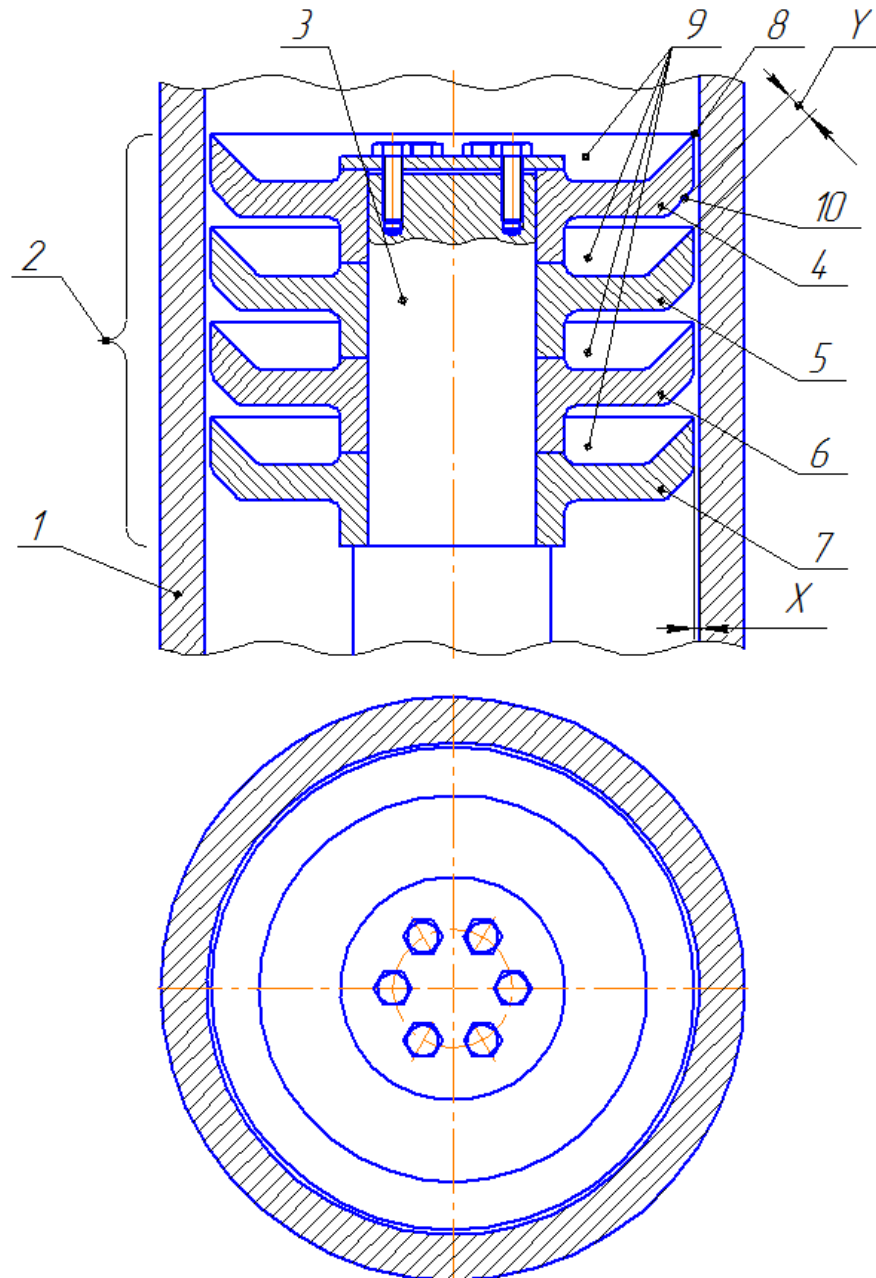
Циліндро-поршнева група крейцкопфного дизельного двигуна: 1 – циліндрова втулка; 2 – поршень; 3 – напрямний шток; 4, 5, 6, 7 – диски; 8 – гострі кромки; 9 – западини; 10 – фаски; X, Y – зазори
